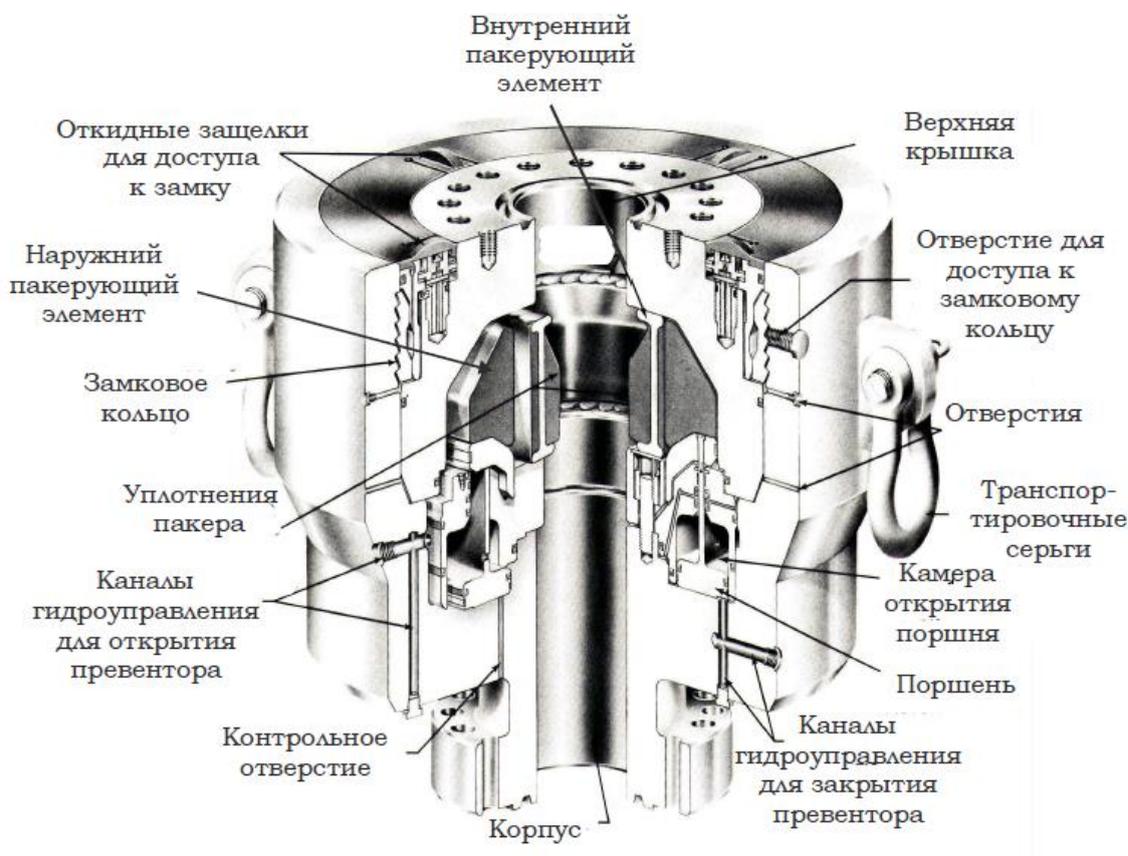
Конструкция превентора фирмы Самсон модель D с двумя пакерующими элементами
